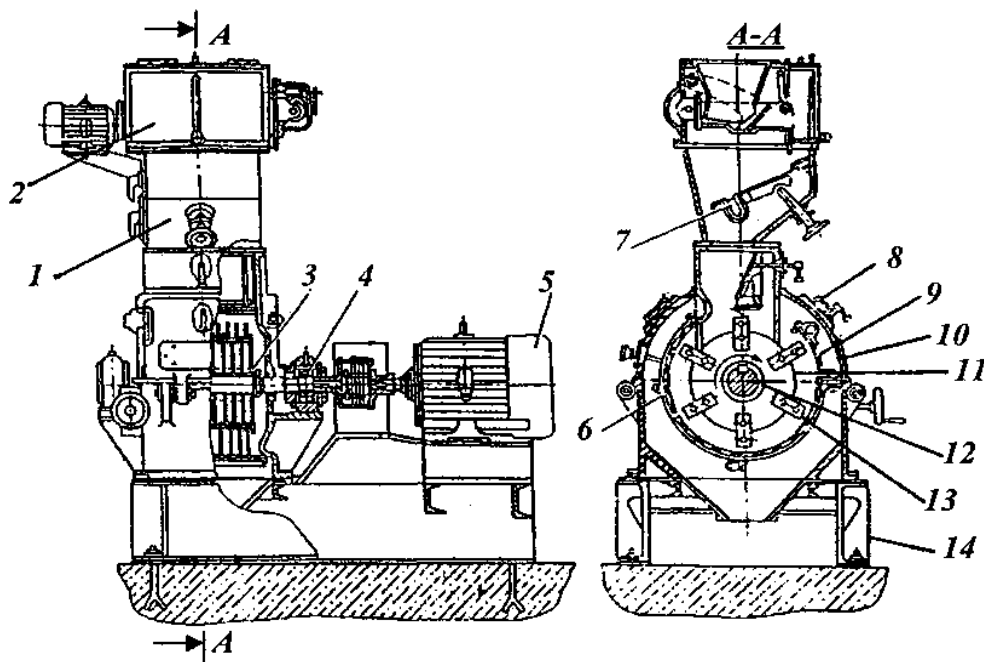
Дробарка молоткова: 1 - корпус; 2 - бункер; 3 - ротор; 4 - вузол підшипниковий; 5 - електродвигун; 6 - сито; 7 - сепаратор магнітний; 8 - гвинт регулюючий; 9 - дека; 10 - кришка; 11 - диск; 12 - кільця; 13 - молоток; 14 - рама.
